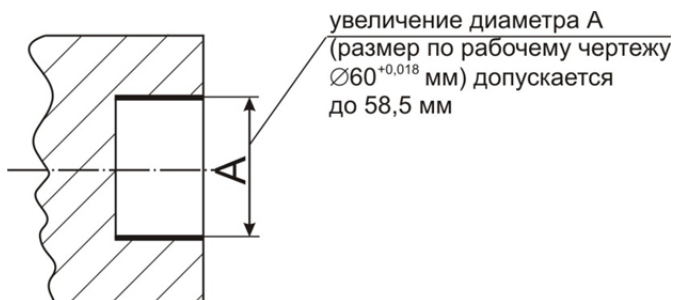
Подготовка детали к ремонту способом дополнительной ремонтной детали
